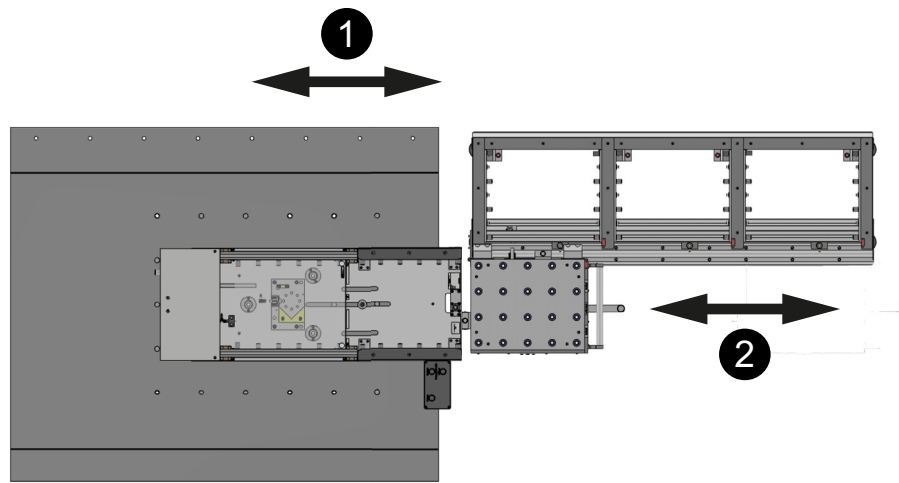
Navetta stazione navetta trasversale (figura esemplificativa)
